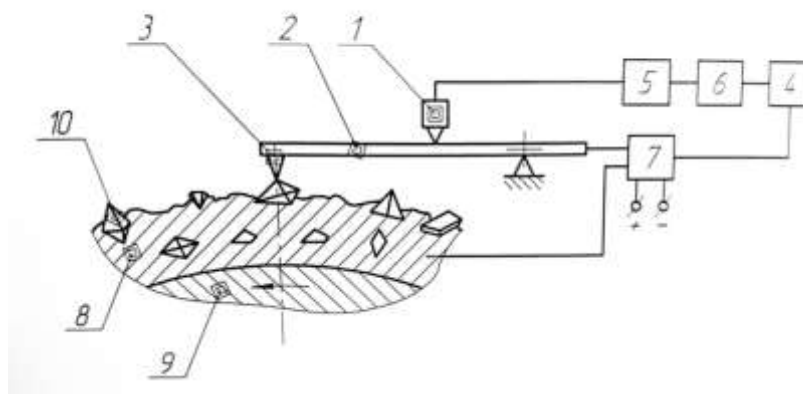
Схема устройства для регистрации рельефа режущей поверхности алмазных кругов на металлической связке
